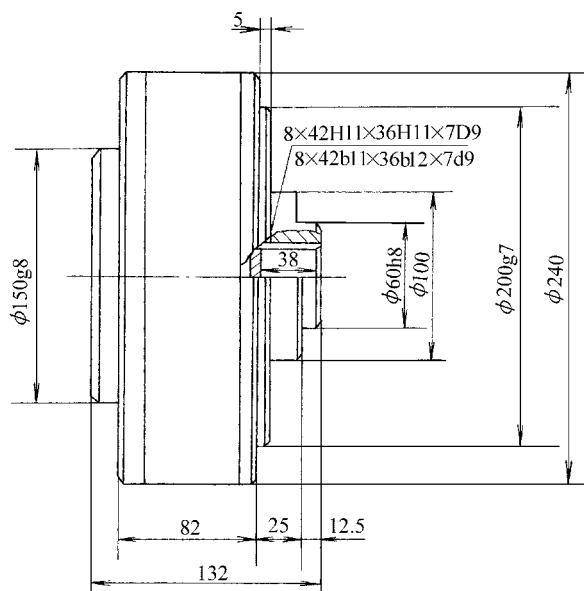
1QJM1A1 型定量马达外形尺寸
